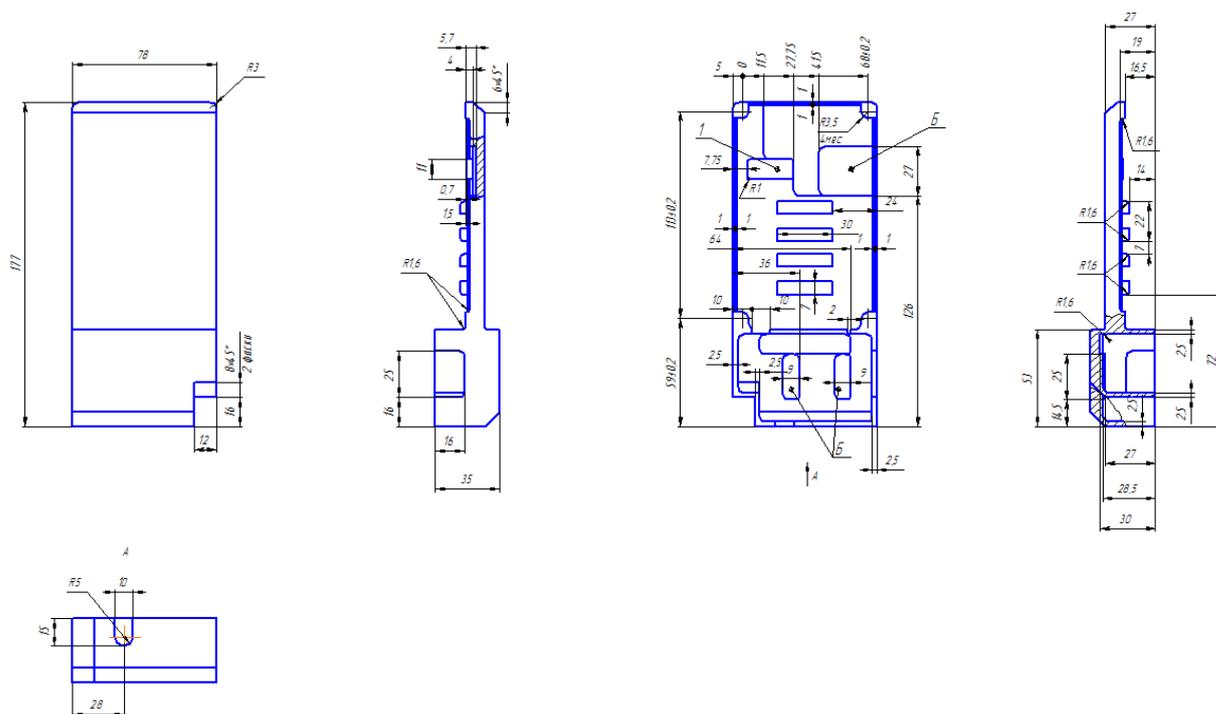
Эскиз заготовки корпуса координатно-измерительной машины Mora Primus
